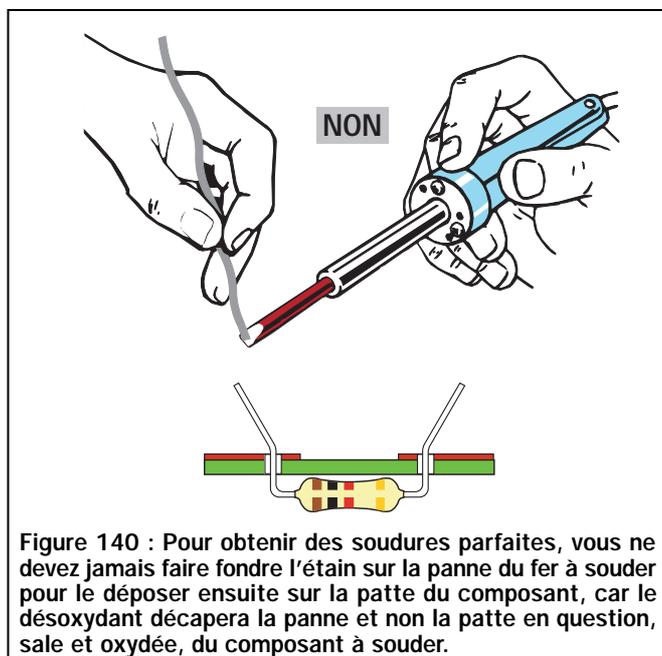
Pour obtenir des soudures parfaites, vous ne devez jamais faire fondre l'étain sur la panne du fer à souder pour le déposer ensuite sur la patte du composant, car le désoxydant décapera la panne et non la patte en question, sale et oxydée, du composant à souder.
